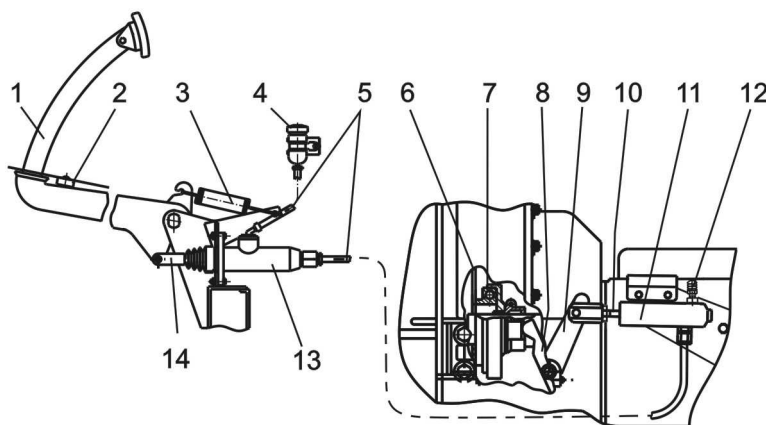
Привод сцепления автобуса ПАЗ-32053-07
